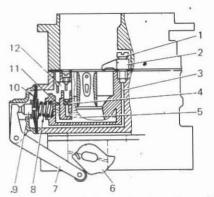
Esquema de la bomba de aceleración del carburador 2107-1107010:
